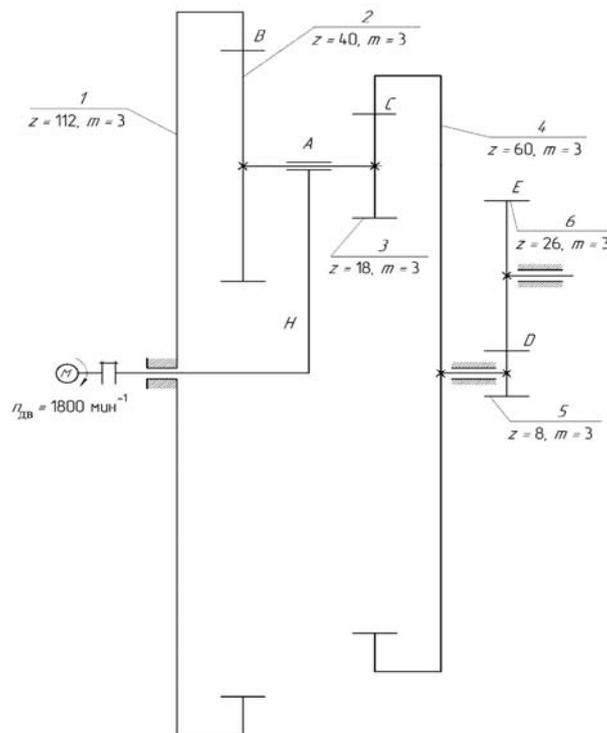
Кинематическая схема зубчатого механизма
